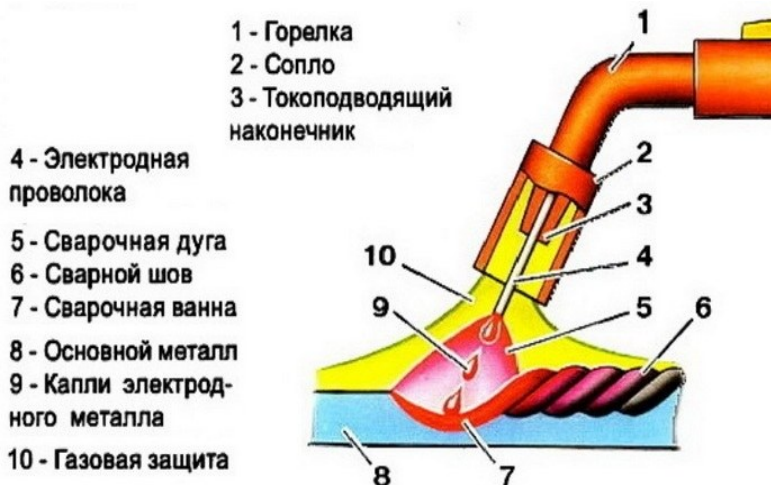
Схема работы полуавтоматической сварки
